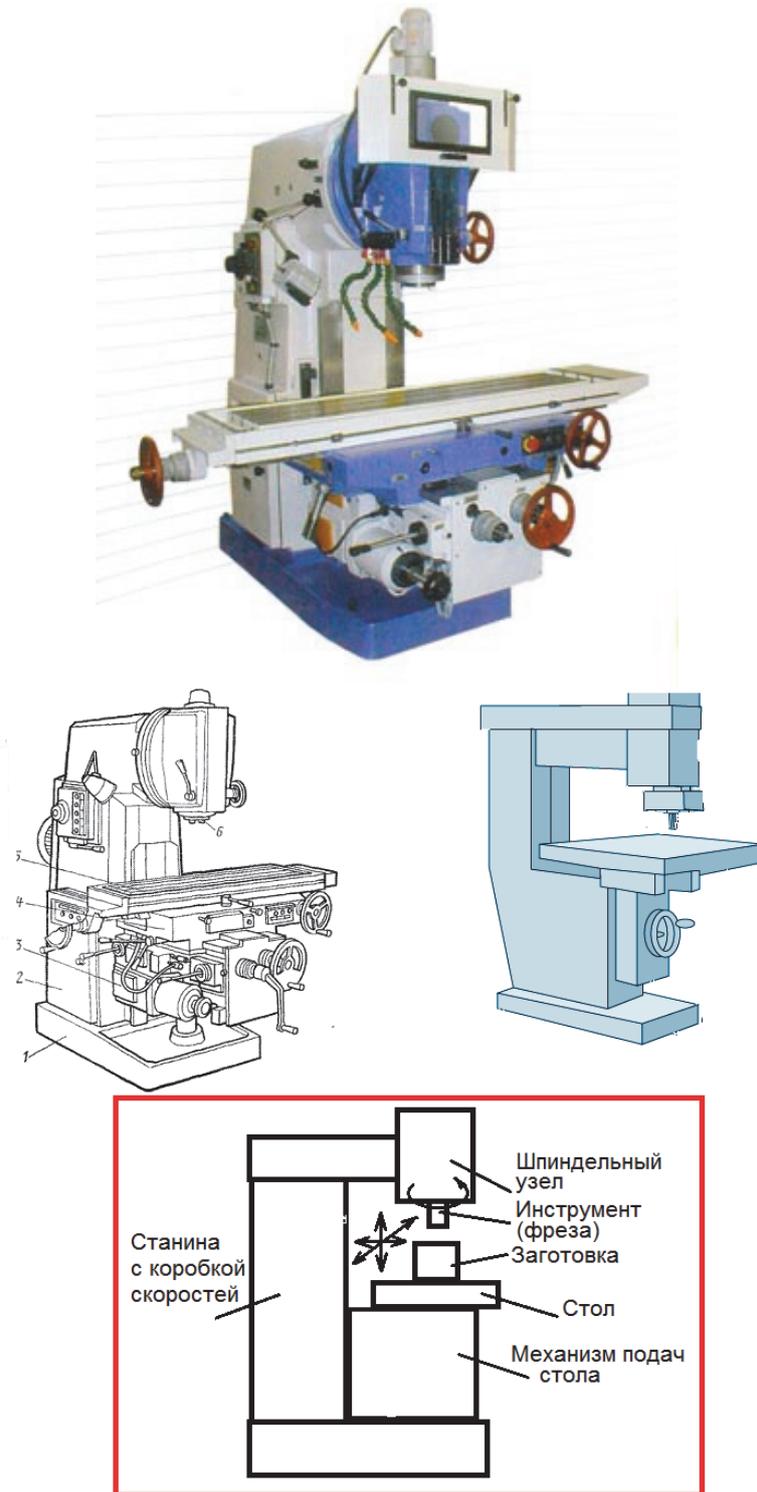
Вертикально фрезерный станок и его схематические представления
